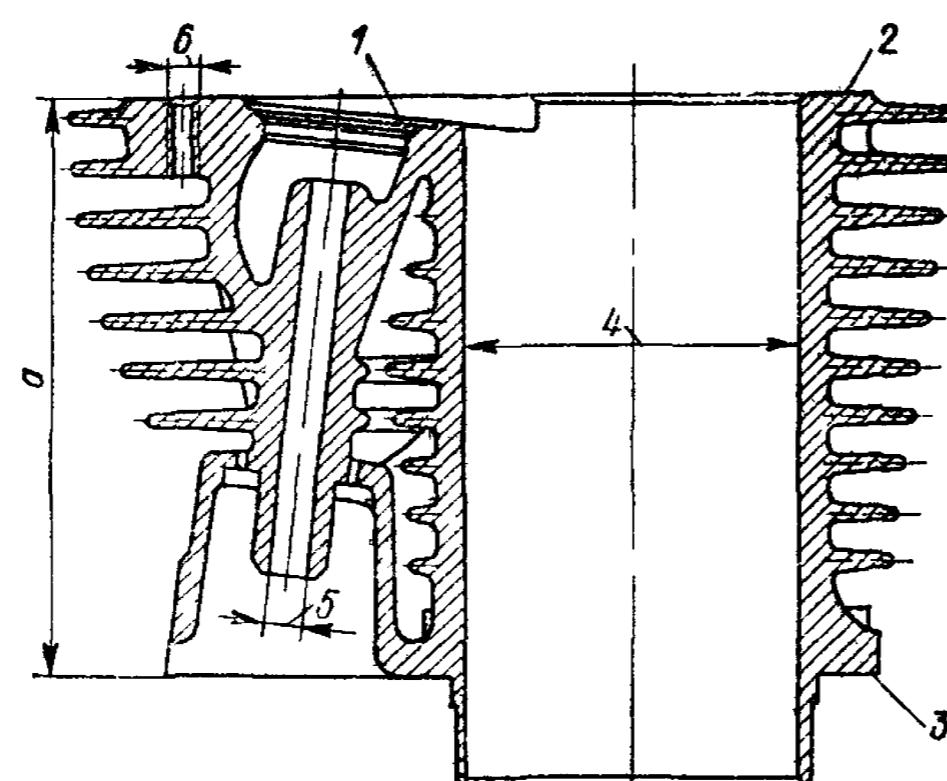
Цилиндр двигателя мотоциклов «Днепр-12» и К-750М
